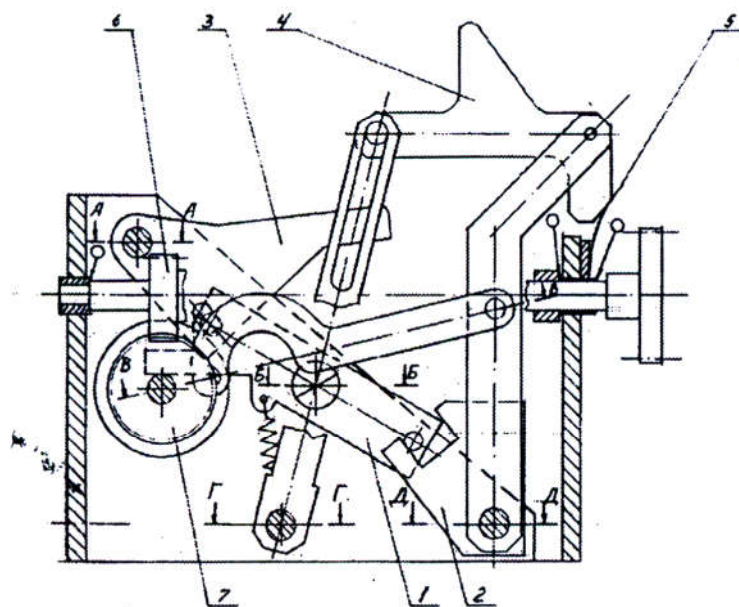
Схема механизма перемещения упаковочного контейнера
